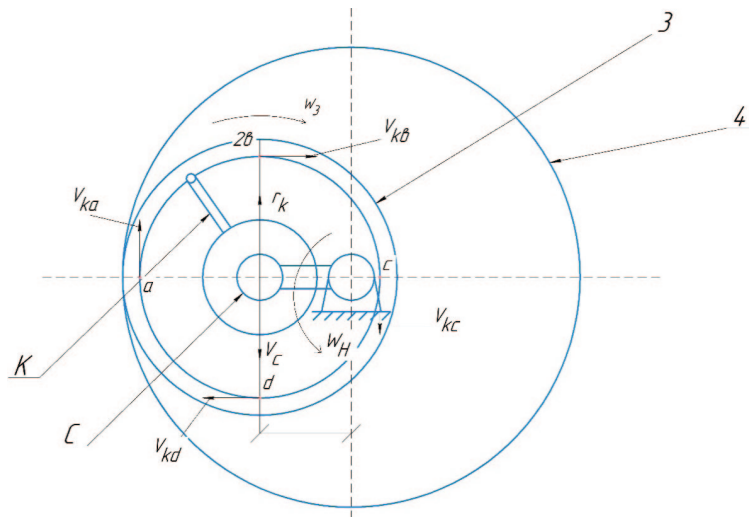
Вид сверху на планетарный привод Шумахера
